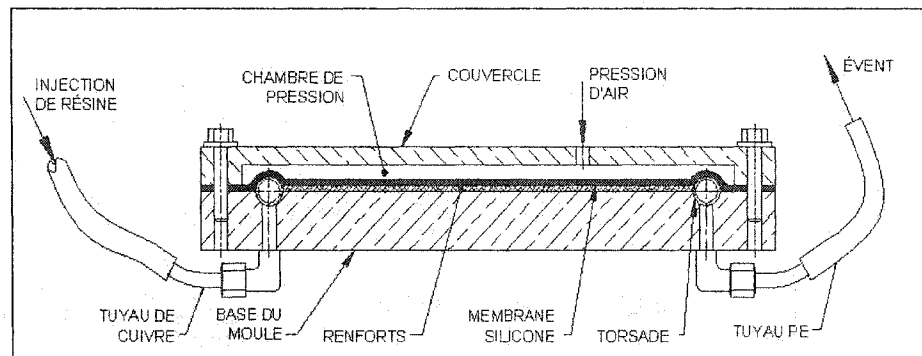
Vue en coupe du montage de fabrication des plaques à renforts tressés
